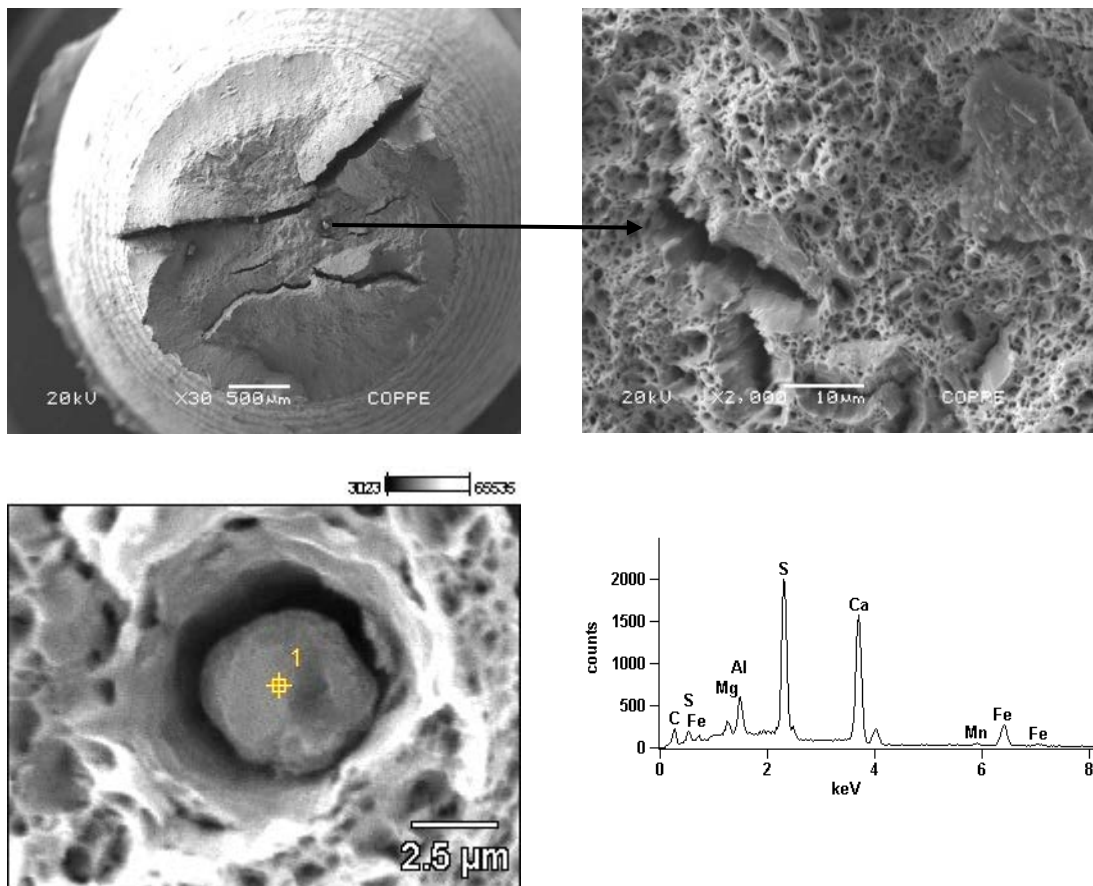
Superfícies de fratura para o aço 2,25Cr-1Mo-0,25V na condição 1C-E600 e inclusões não metálicas.
